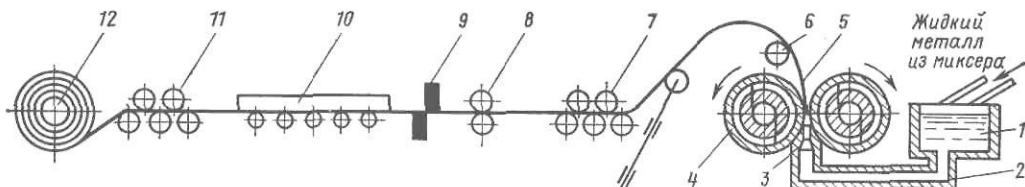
Непрерывный агрегат бесслитковой прокатки алюминиевой полосы 8×1600 мм
